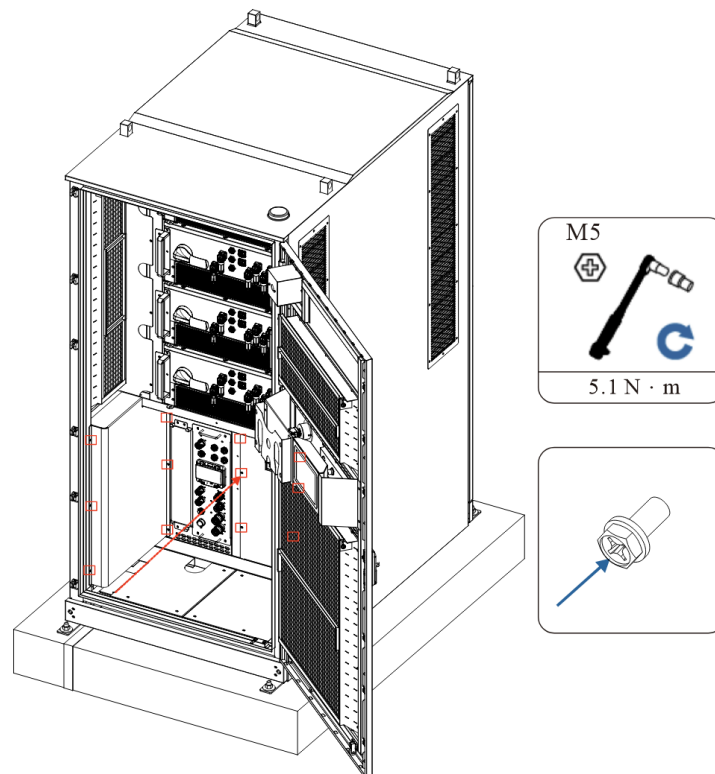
Installieren Sie die AC/DC-Schutzplatten wieder
